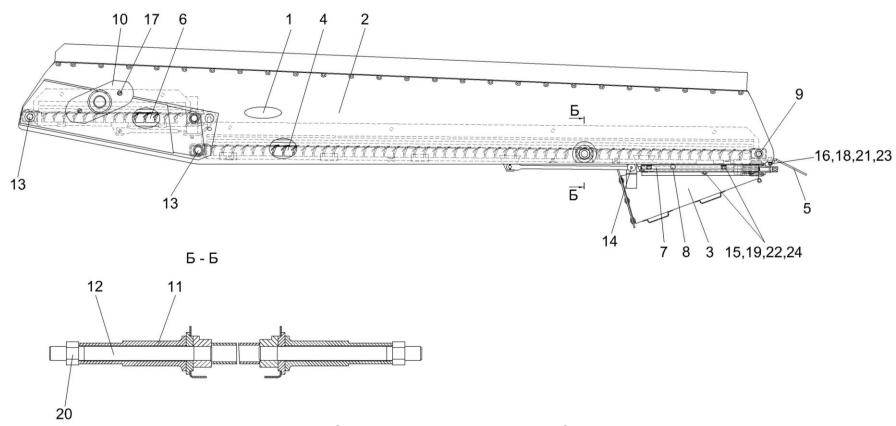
Стан решетный верхний КЗК-10-0260000
